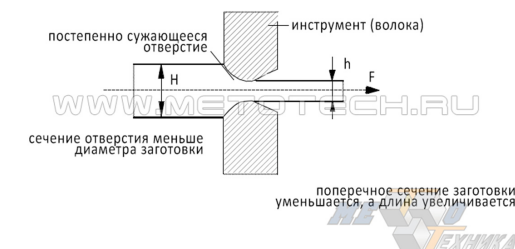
Принцип волочения: протяжка заготовки сквозь фильеру волоки
